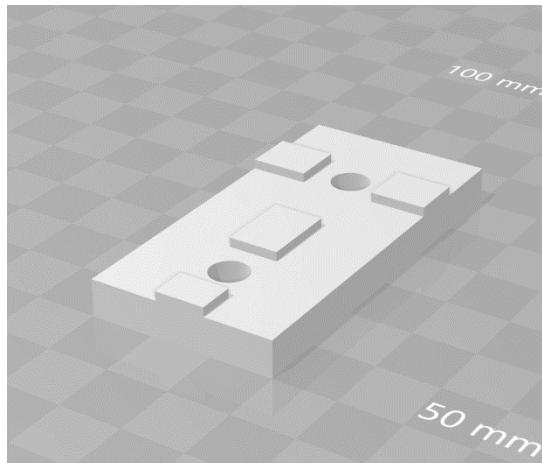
Uchycení motoru spodní levé Autor: David Trcka
